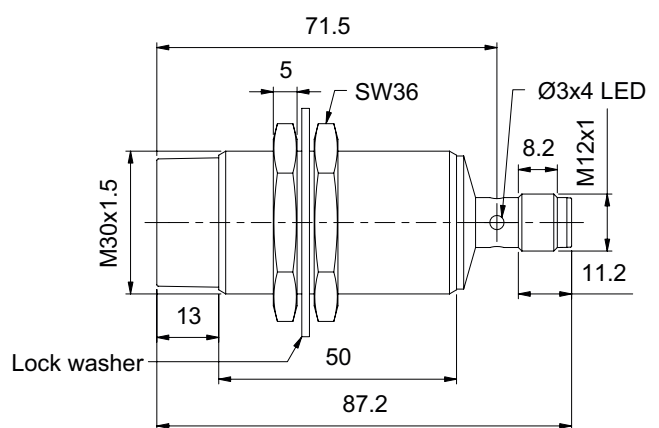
Uskærmet, ikke planmontage, M12-stik
